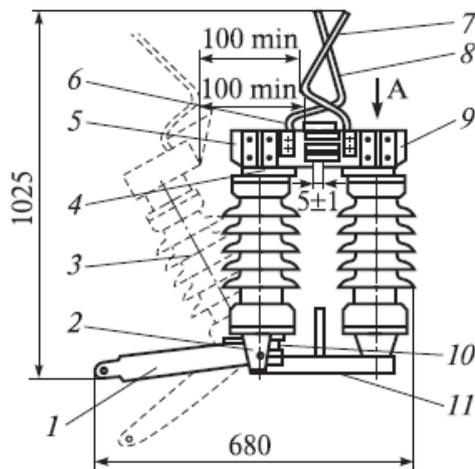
Разъединитель контактной сети постоянного тока РКС-3,3/3000: 1 – рычаг; 2 – подвижный кронштейн; 3 – подвижный изолятор; 4 – нож подвижный; 5 – кронштейн; 6 – кожух; 7, 8 – дугогасящие рога; 9 – нож неподвижный; 10 – упор; 11 – основание.
